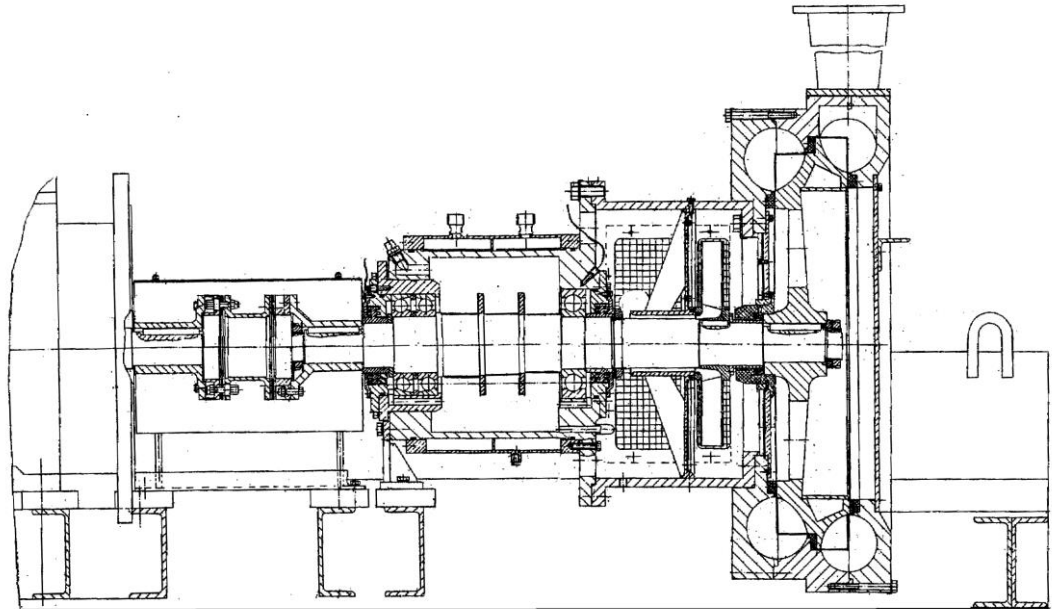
Схема компресора вихрового ВВ 12/1-1,6.
